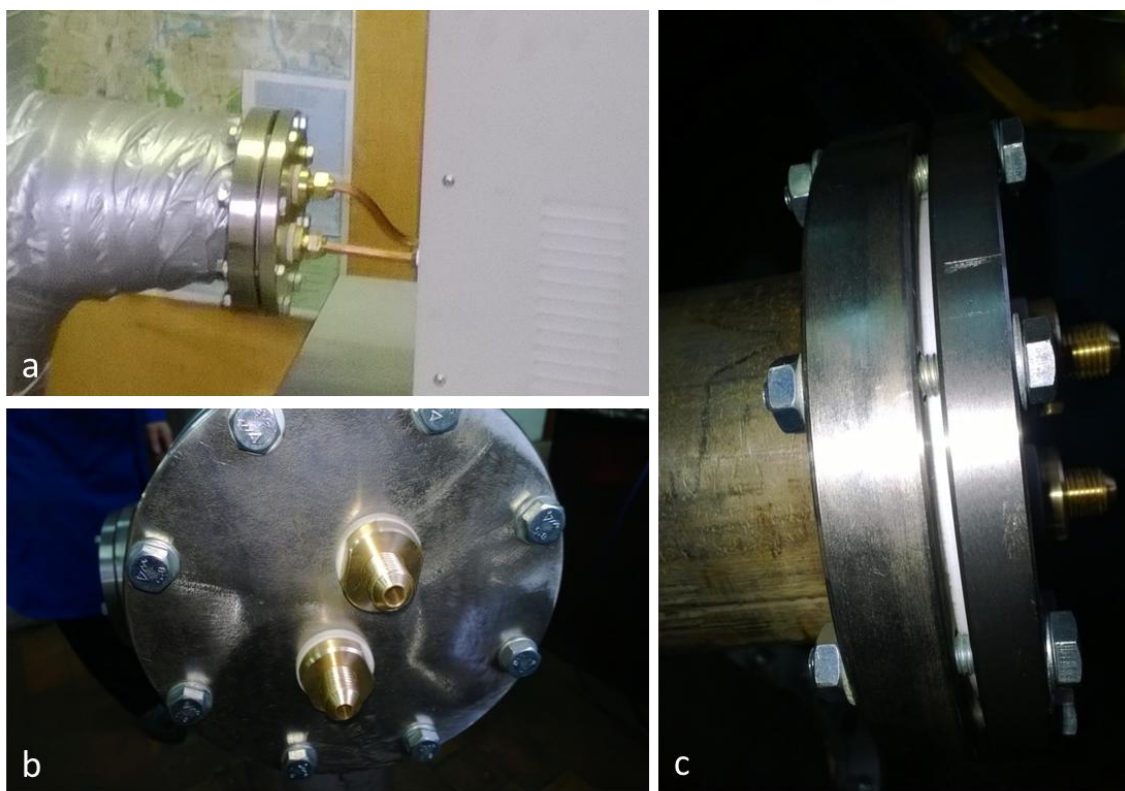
Ввод катушки индуктора: а) крепление индуктора к катушке через фланец накидными гайками, б) ответный фланец (фронтальный вид), с) соединение фланцев (вид сбоку).
